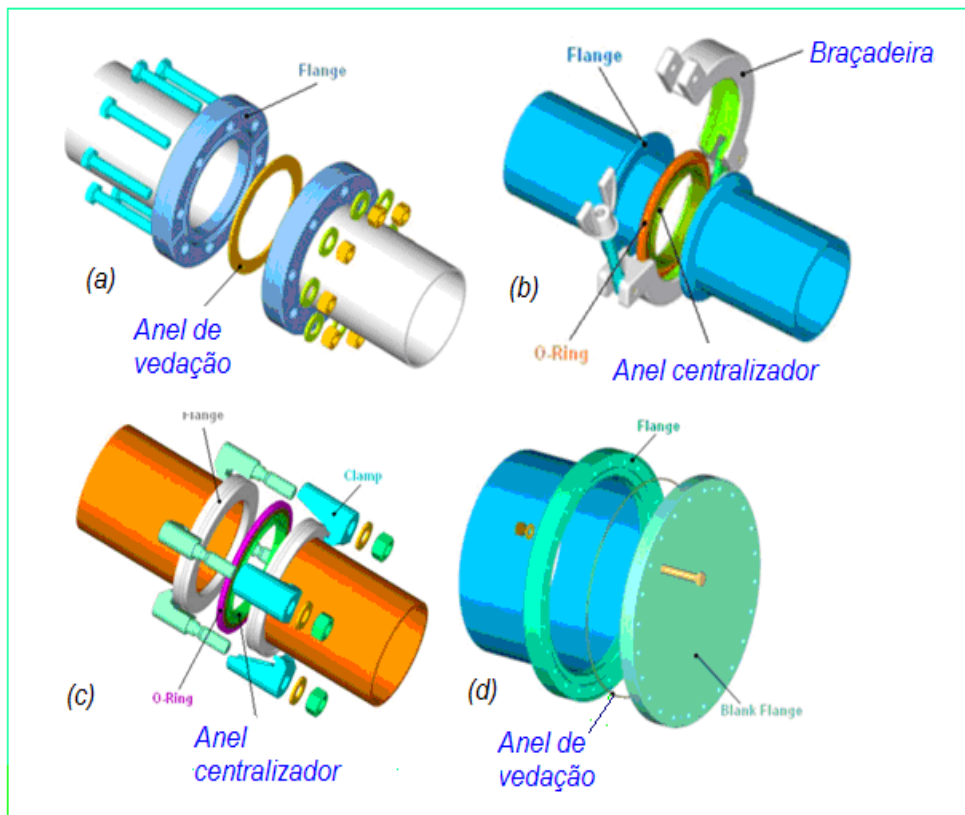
Detalhamento da montagem dos componentes auxiliares do sistema de vácuo: (a) CF/Conflat 16-400mm; (b) ISO-KF 0 – 50 mm; (c) ISO-K 63 -630 mm; (d) Wire Seal Flange 250 – 600 mm. Fonte: [www.nd.edu/~nsl/Lectures/urls/Introduction\\_to\\_vacuum\\_gauges.pdf](http://www.nd.edu/~nsl/Lectures/urls/Introduction_to_vacuum_gauges.pdf), acesso em 15/01/2009.
